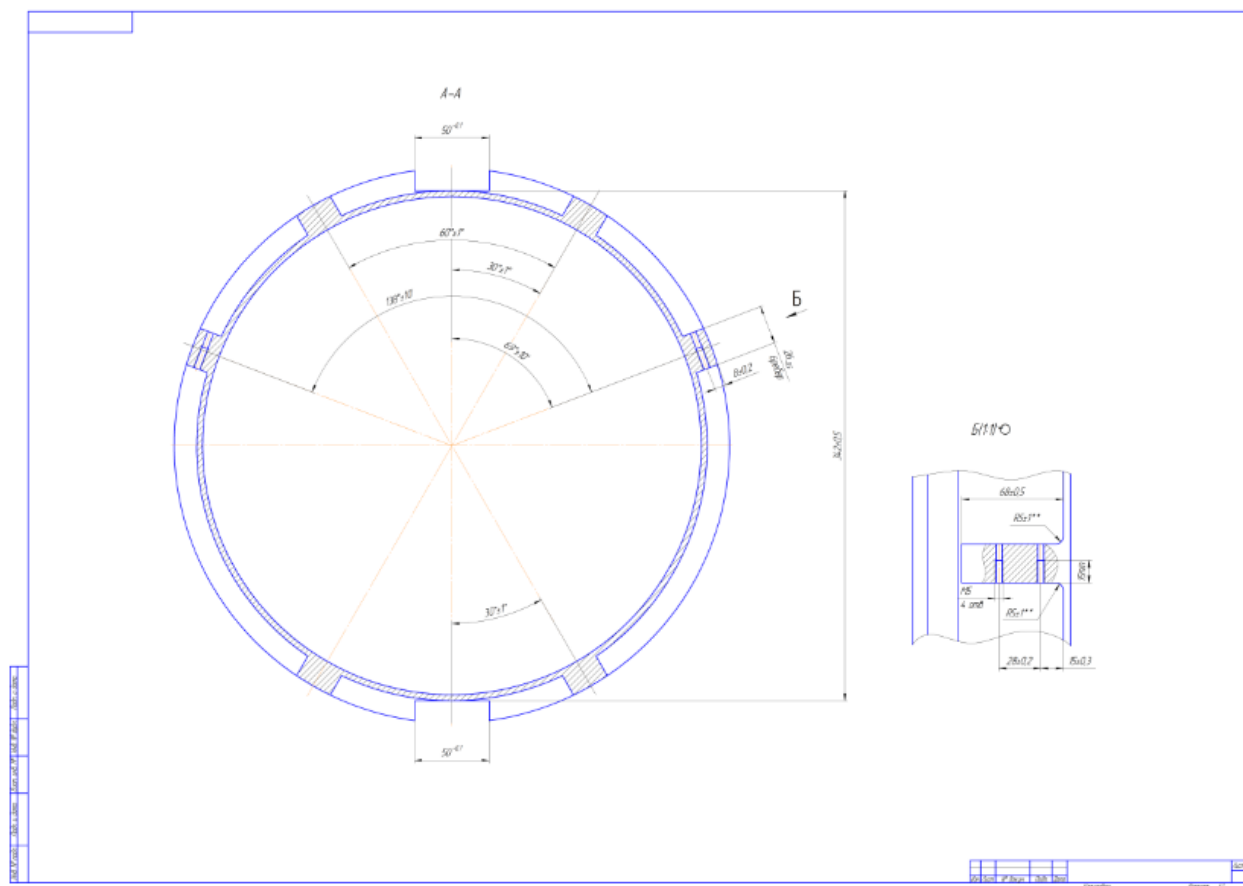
Чертеж детали «Корпус». Сечение А-А
